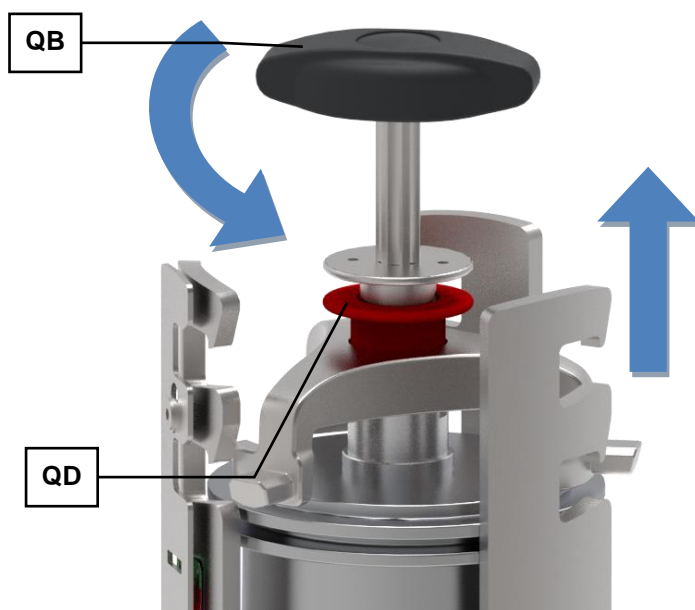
Sbloccaggio dell'unità di serraggio della giara di macinazione
